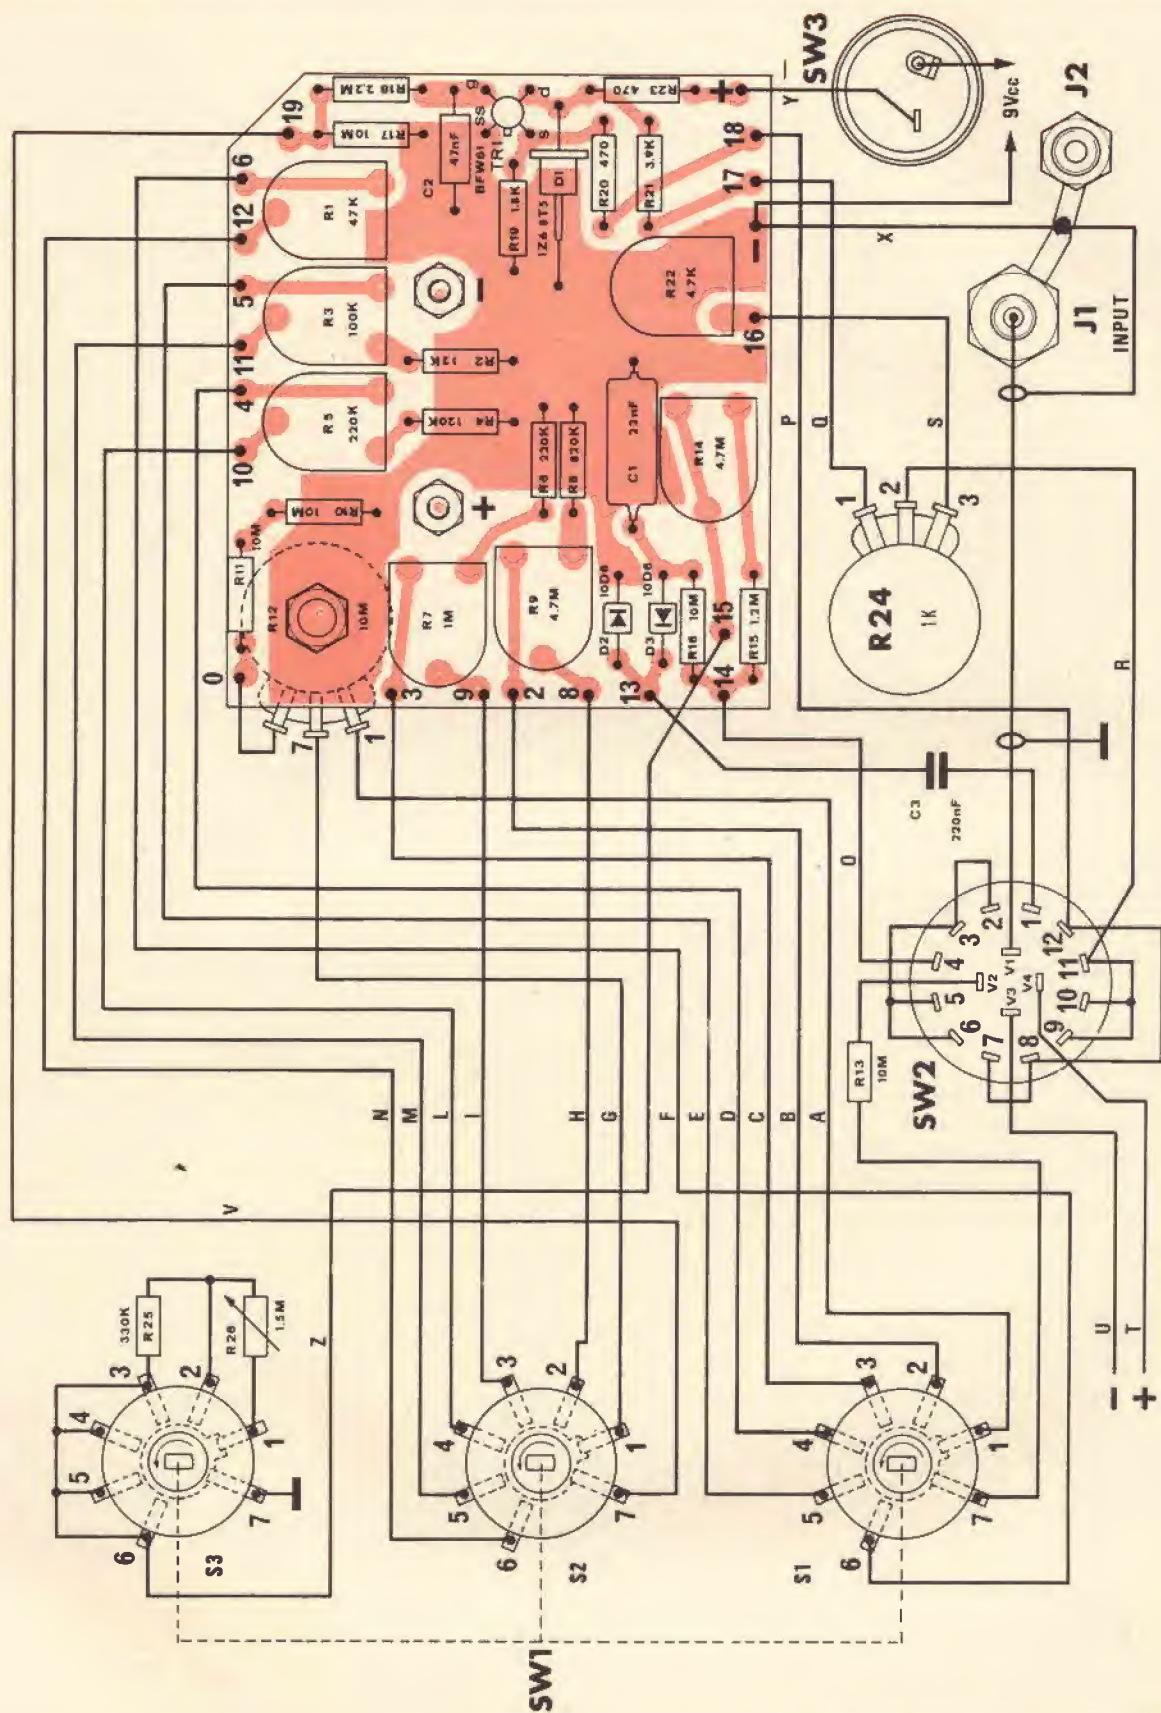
Cablaggio fra circuito stampato e componenti esterni.
